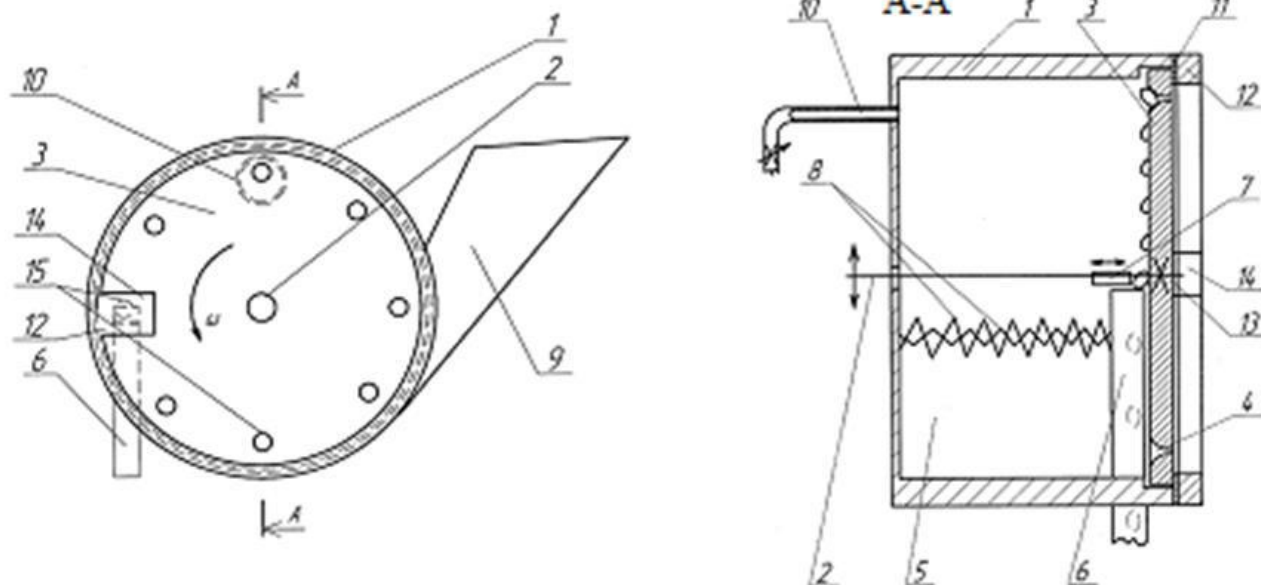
Висівний апарат 1 – корпус; 2 – приводний вал; 3 – висівний диск; 4 – дозувальний елемент; 5 – насіннєва камера; 6 – трубка забірною пристрою; 7 – регулювальний механізм; 8 – пружний елемент; 9 – бункер; 10 – канал подачі повітря; 11 – прокладка; 12 – кришка; 13 і 14 – виступи; 15 – насіння.
